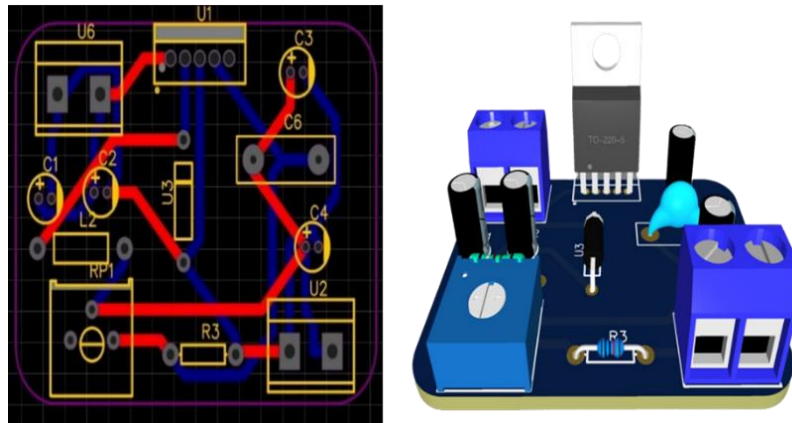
Diseño Esquemático PCB y vista 3D convertidor fijo.
